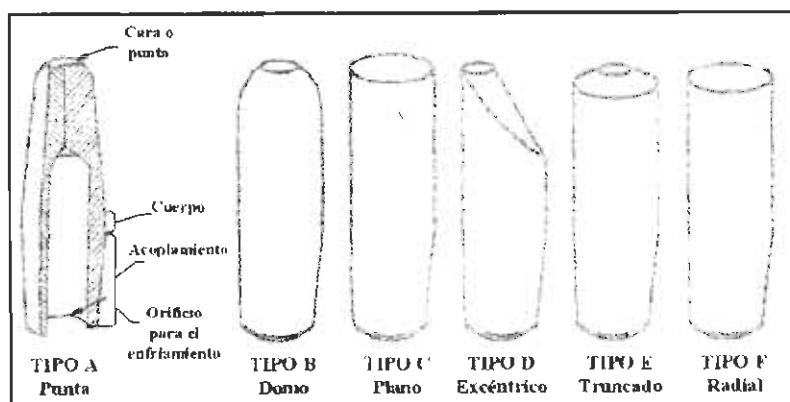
Geometrías de electrodos para soldadura por puntos ^[13]
